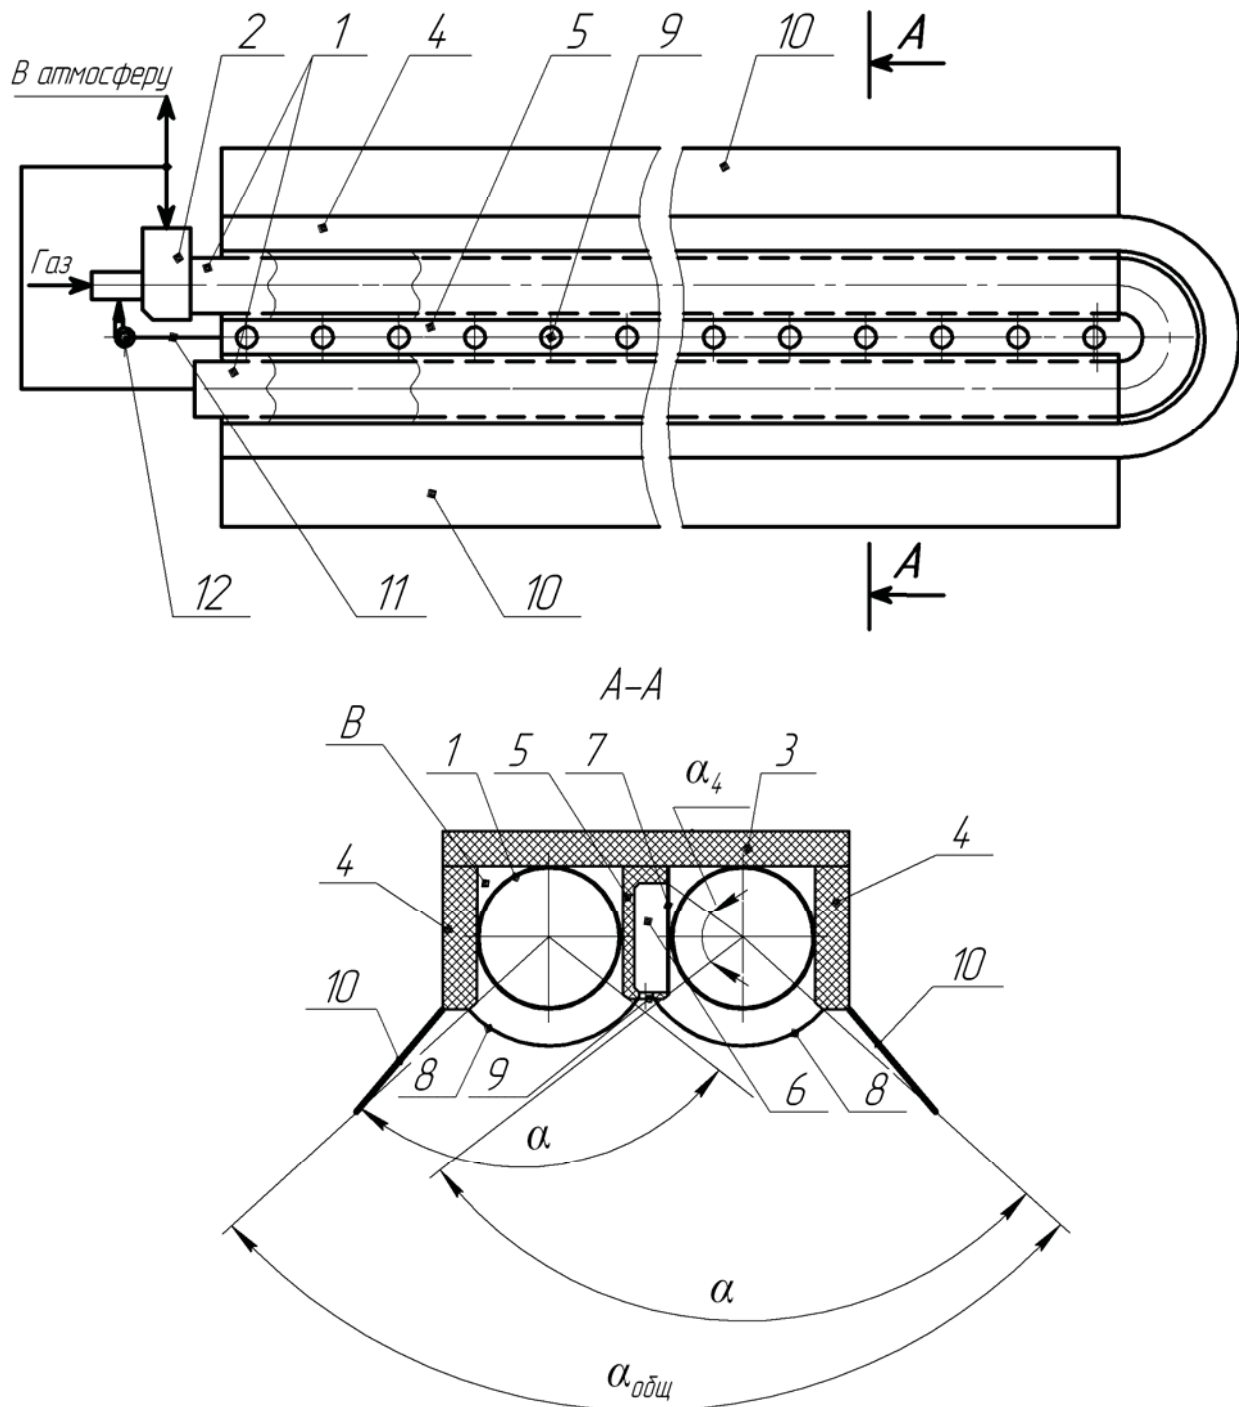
Схема нового ленточного газового инфракрасного нагревателя с двойным теплоизлучающим контуром: 1 – двойной ленточный трубчатый излучатель; 2 – газогорелочный блок с горелкой, камерой рециркуляции, центробежным вентилятором и дымоходом; 3 – верхняя панель теплоизоляции; 4 – боковые панели теплоизоляции; 5 – промежуточная панель теплоизоляции; 6 – продольный воздушный канал; 7 – металлическая стенка канала; 8 – радиальные ленточные отражающие панели; 9 – отверстия в промежуточной панели; 10 – боковые отражатели тепловых потоков; 11 – патрубок; 12 – вентилятор
